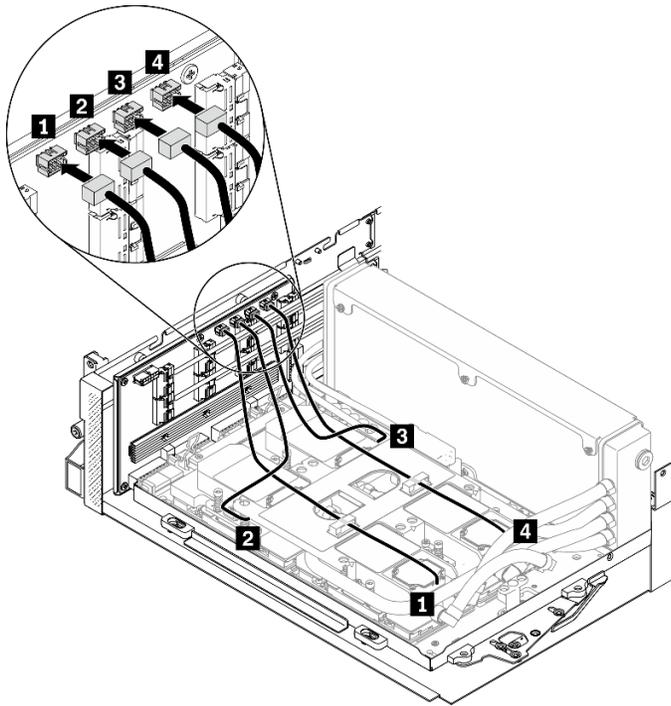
Cheminement des câbles de pompe d'assemblage de plaque froide vers l'assemblage de resynchroniseur - Configuration G
